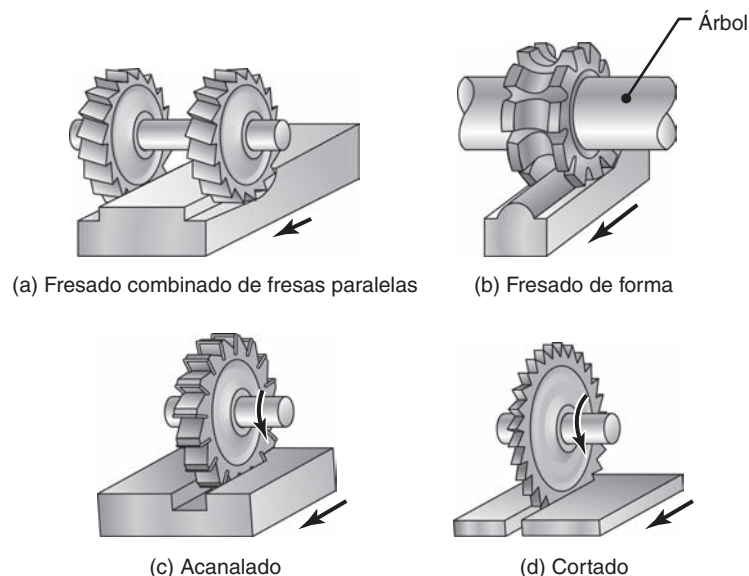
Cortadores para (a) fresado combinado de fresas paralelas; (b) fresado de forma; (c) acanalado, y (d) cortado con un cortador de fresado.
